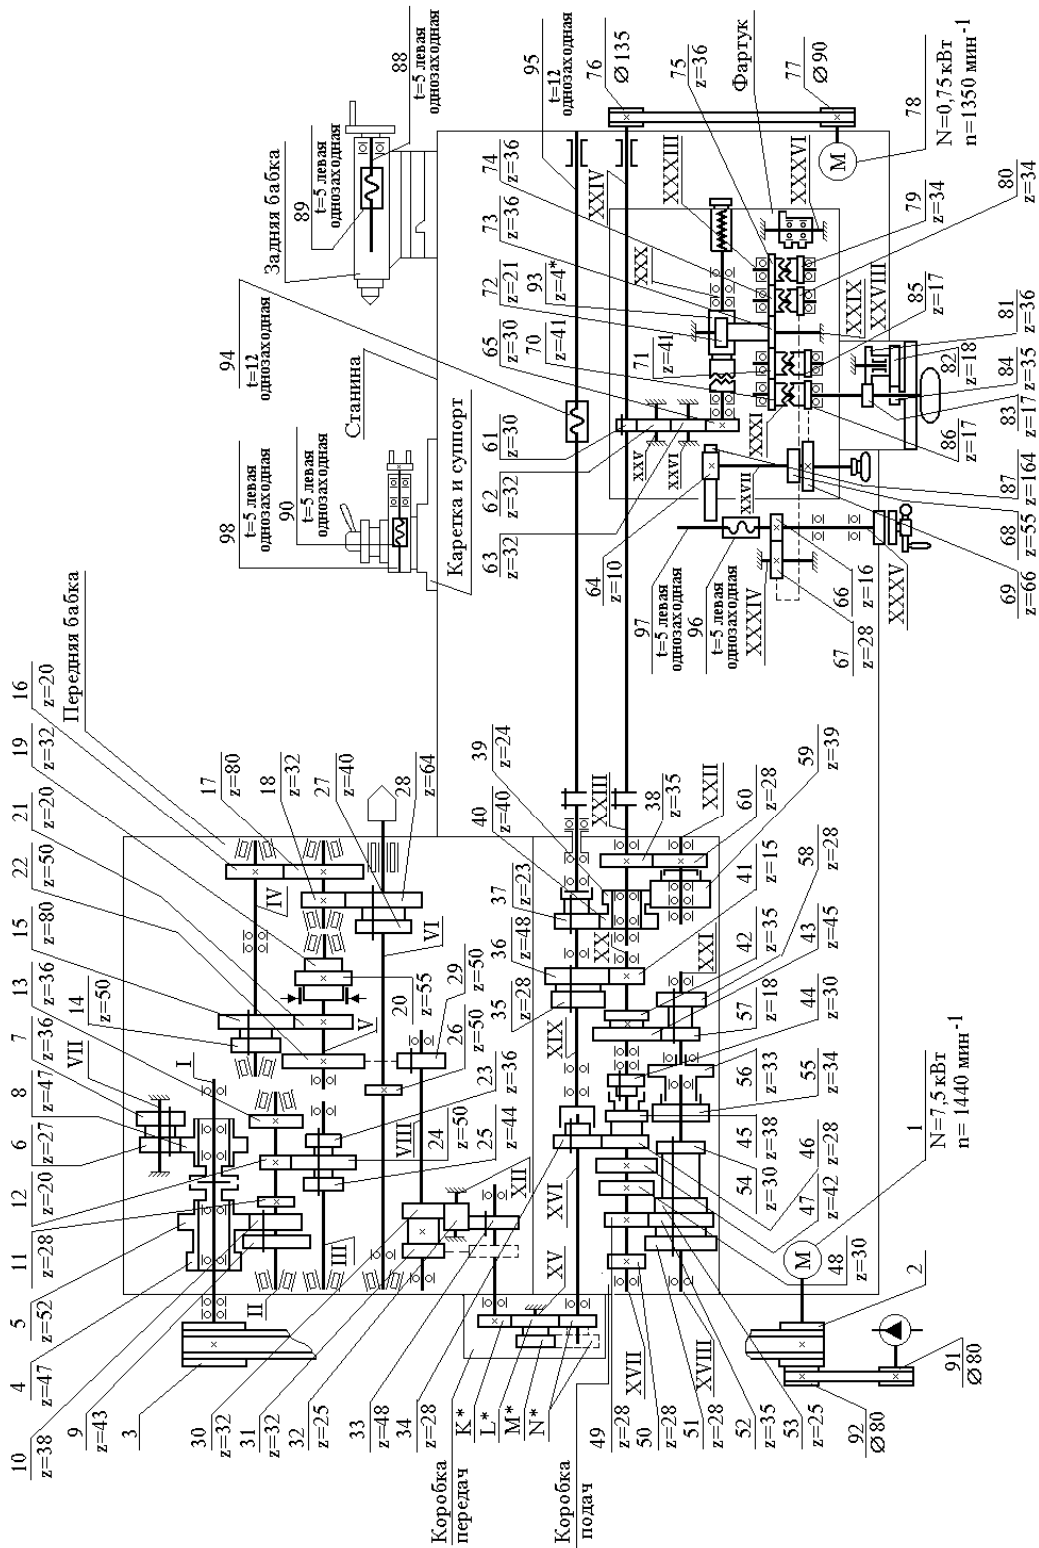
Кинематическая схема станка 16В20, 1В62Г
